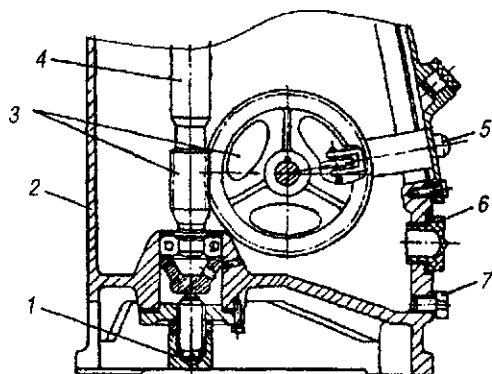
Схема механизма регулировки вертикального вала: 1 – регулировочный винт; 2 – станина; 3 – приводной механизм; 4 – вертикальный вал (веретено); 5 – кнопка пульсатора; 6 – смотровое стекло; 7 – отверстие для слива масла
